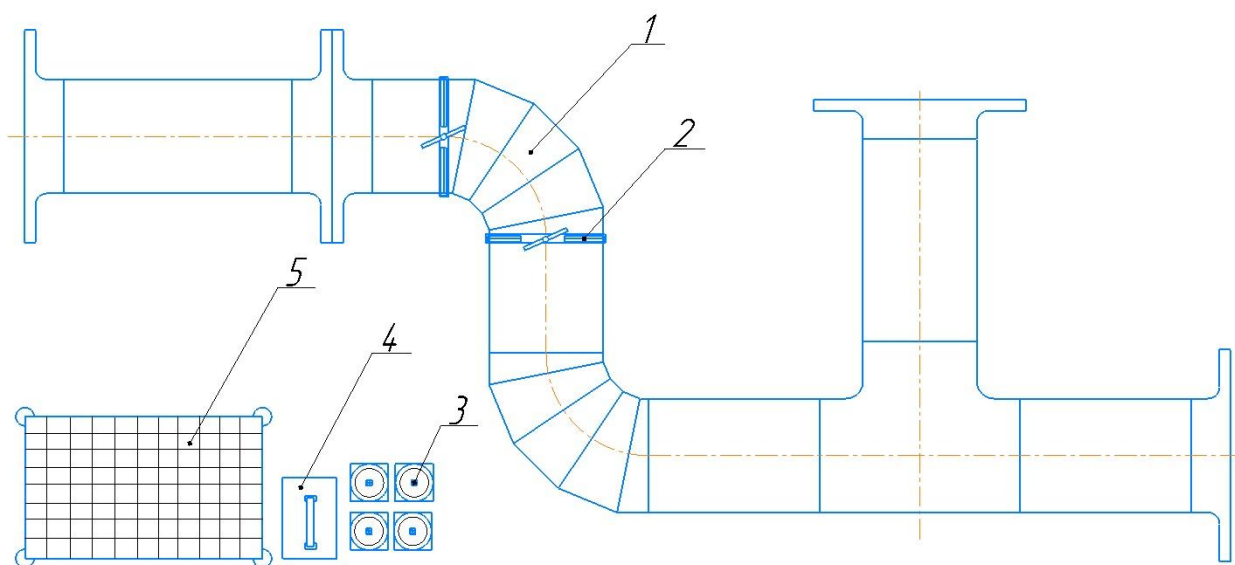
Схема сварочно-ремонтного участка в условиях ТЭЦ
